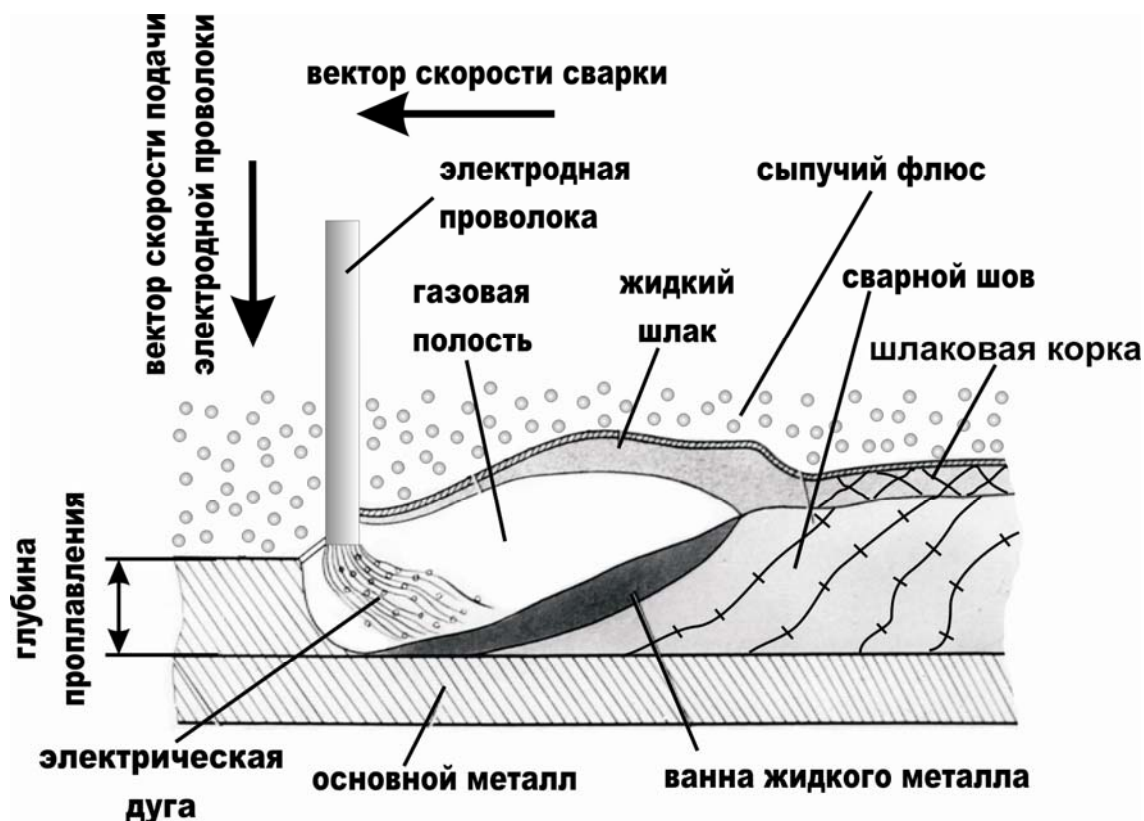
Схема процесса автоматической сварки под флюсом
